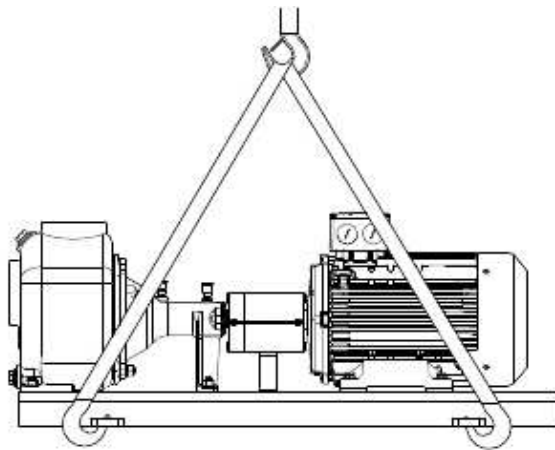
Richtiges Anheben eines kompletten Pumpenaggregates mit Motor und Grundrahmen
